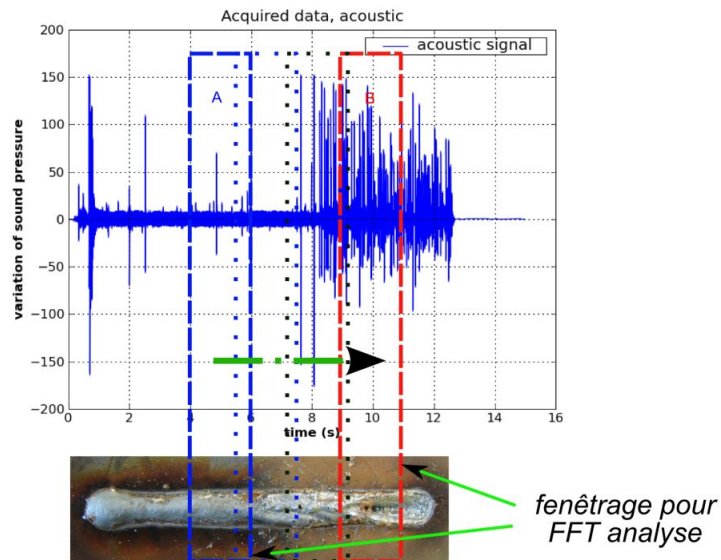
Un défaut apparaît en cours de soudage : signal acoustique et la soudure résultante
